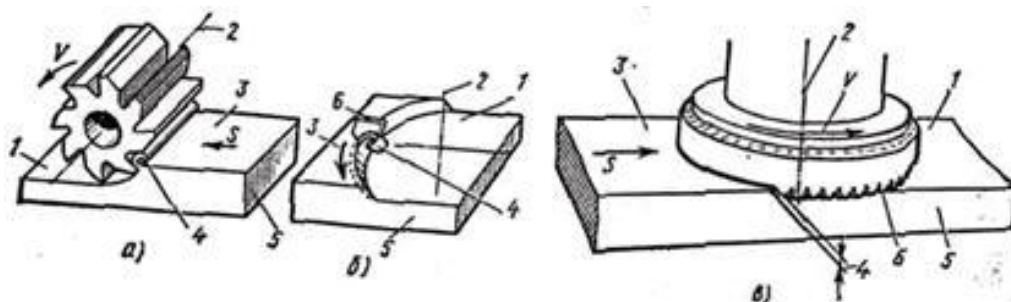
Схемы фрезерования: а — цилиндрическое, б и в — торцовое фрезерование; 1 — обработанная поверхность, 2 — ось вращения фрезы, 3 — обрабатываемая поверхность, 4 — стружка, 5 — заготовка, 6 — нож фрезы.
